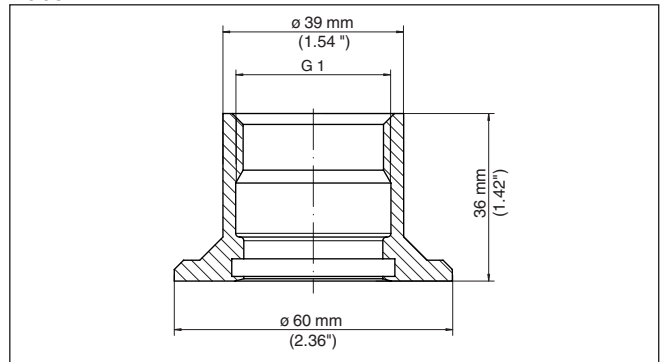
Maße Einschweißstutzen G1 (DIN 3852-A)
